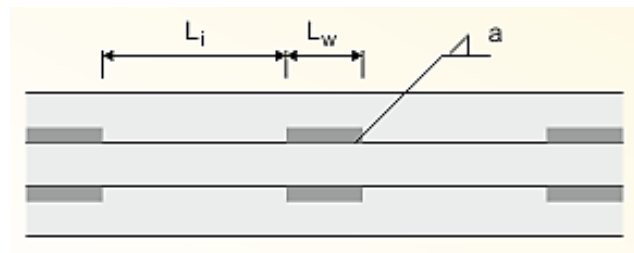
Cordón de soldadura discontinuo. Fuente: Software Craneway
